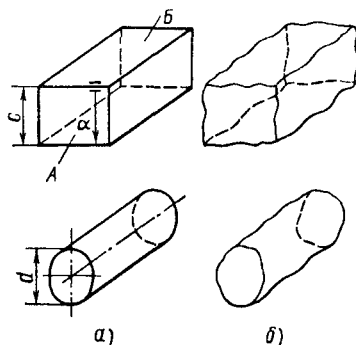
Детали с идеальными поверхностями (а) и реальными поверхностями (б)
